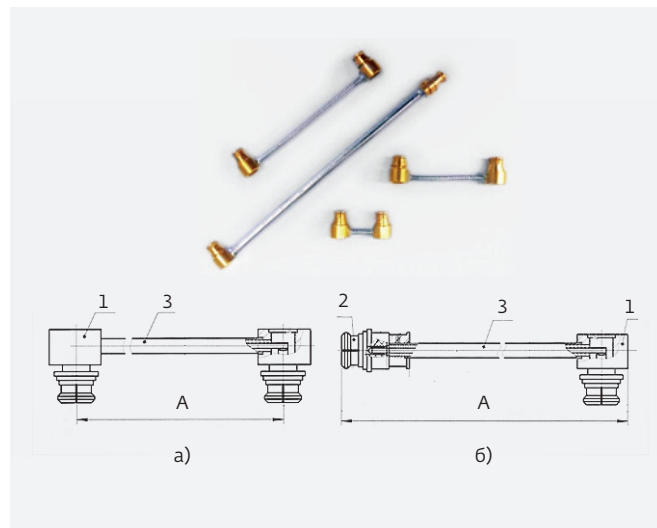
Внешний вид и конструкция кабельных сборок с угловыми соединителями (а), с прямым и угловым соединителями (б). 1 – угловой соединитель, 2 – прямой соединитель, 3 – кабель.
